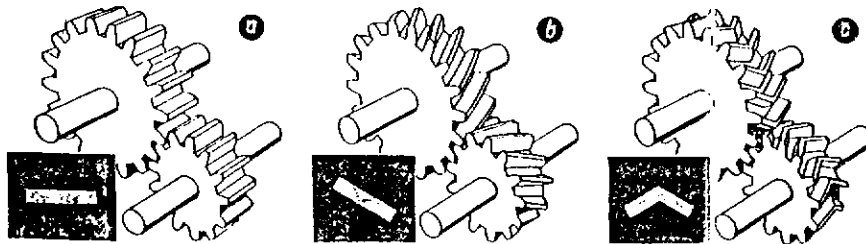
Engranajes de ruedas frontales. a) Ruedas frontales con dientes rectos; b) ruedas frontales con dientes inclinados; c) ruedas frontales con dientes en forma de flecha.
